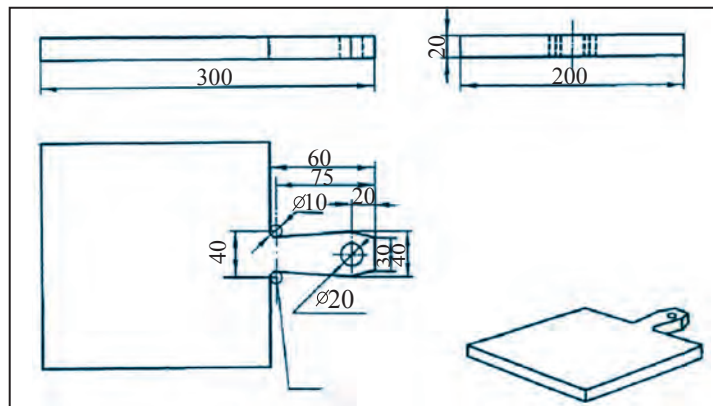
Чертёж изготовления доски для разделывания овощей.
